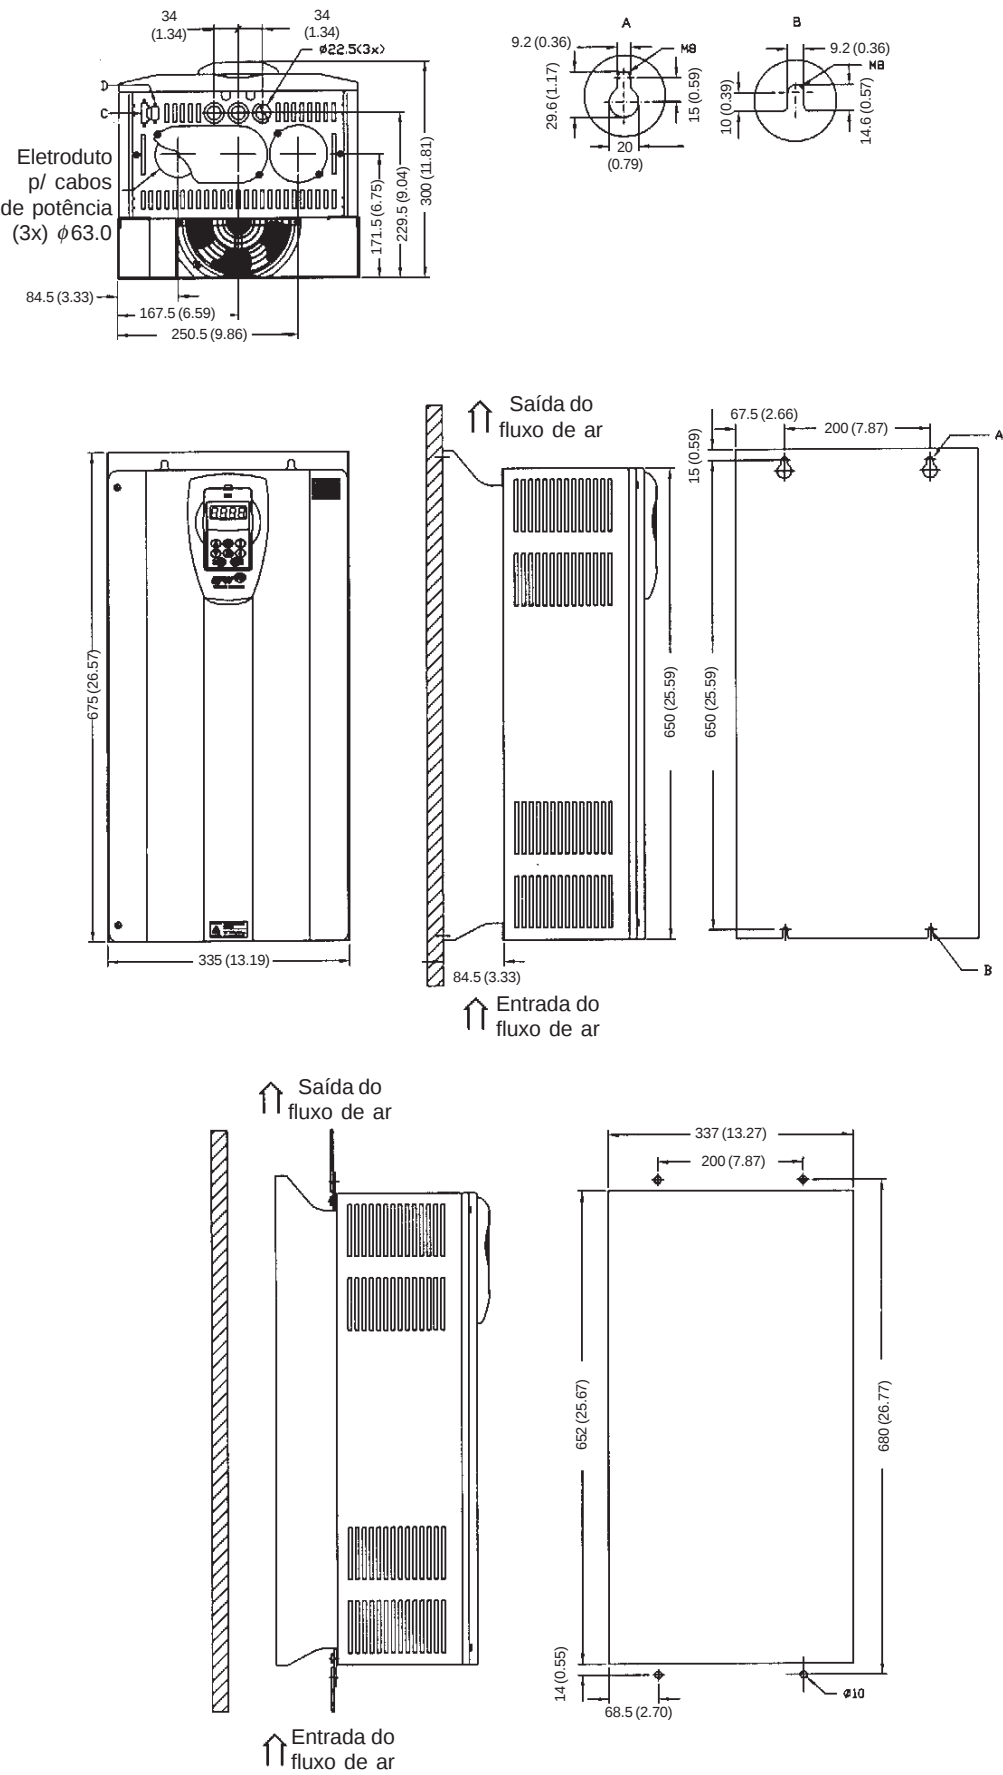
Mecânica 6 - Dimensões em mm (polegadas)
